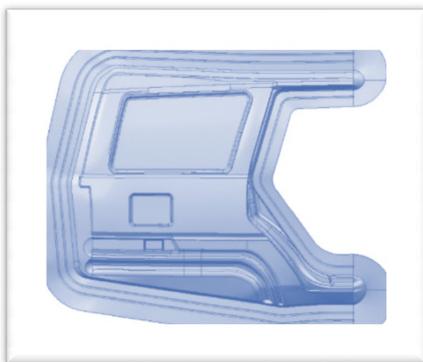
Модель штамповки заднего крыла автомобиля ИЖ-21261
